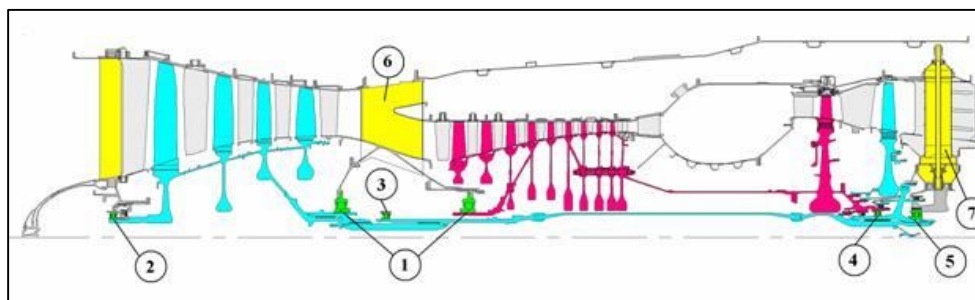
Силовая схема двигателя: 1 – радиально-упорные (шариковые) подшипники; 2 – роликовый подшипник передней опоры КНД; 3 – передний роликовый подшипник вала НД; 4 – межроторный роликовый подшипник; 5 – роликовый подшипник задней опоры ТНД; 6 – промежуточный корпус; 7 – задний стоечный узел
